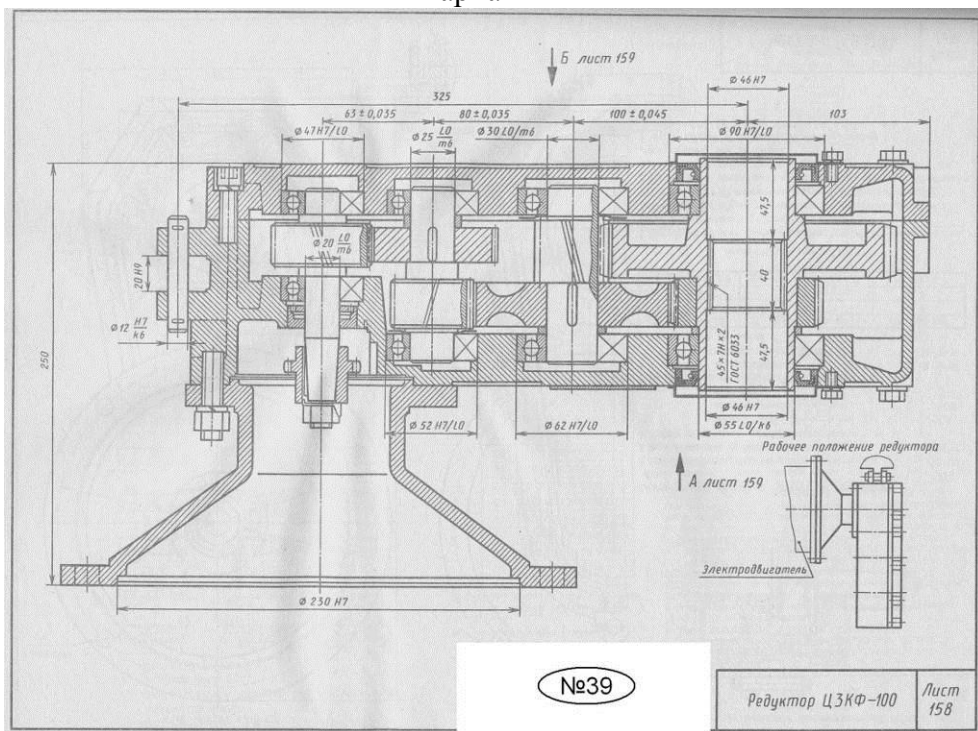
Цилиндрический двухступенчатый соосный редуктор
